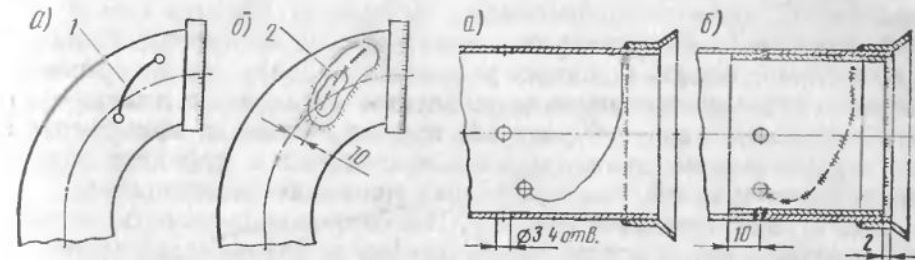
Установка накладки при ремонте сваркой:
